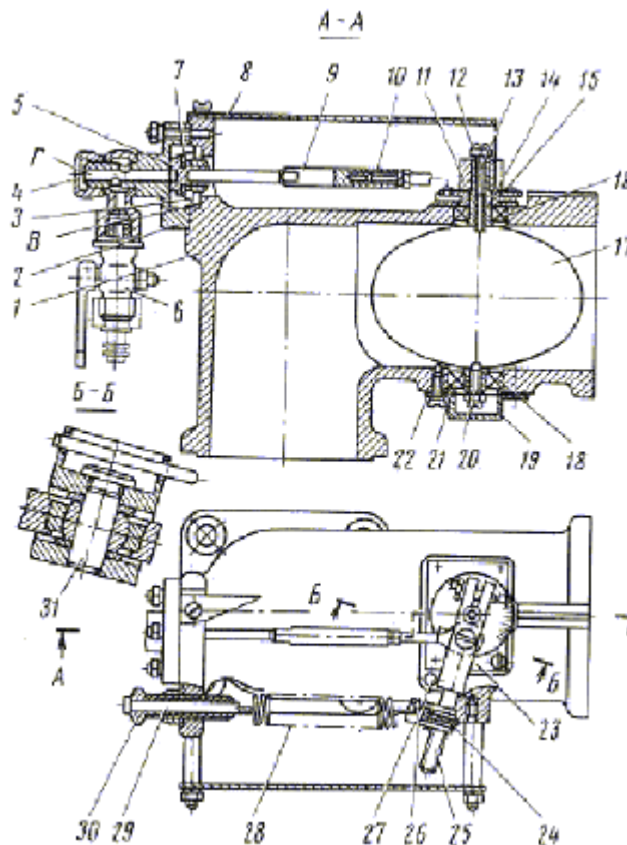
Управляемая заслонка: 1, 2 – корпуса; 3 – мембрана; 4, 12 – гайки; 5, 29 – штоки; 6 – кран; 7 – накладка; 8 – кожух; 9, 10 – тяги; 11 – рычаг; 13, 20 – винты; 14 – валик; 15 – шкала; 16, 18 – подшипники; 17 – заслонка; 19, 23 – крышки; 21 – кольцо; 22 – прокладка; 24 – ролик; 25 – шпилька; 26 – серьга; 27 – штифт; 28 – пружина; 30 – втулка; 31 – ось; В – торец; Г – полость для подвода воды
